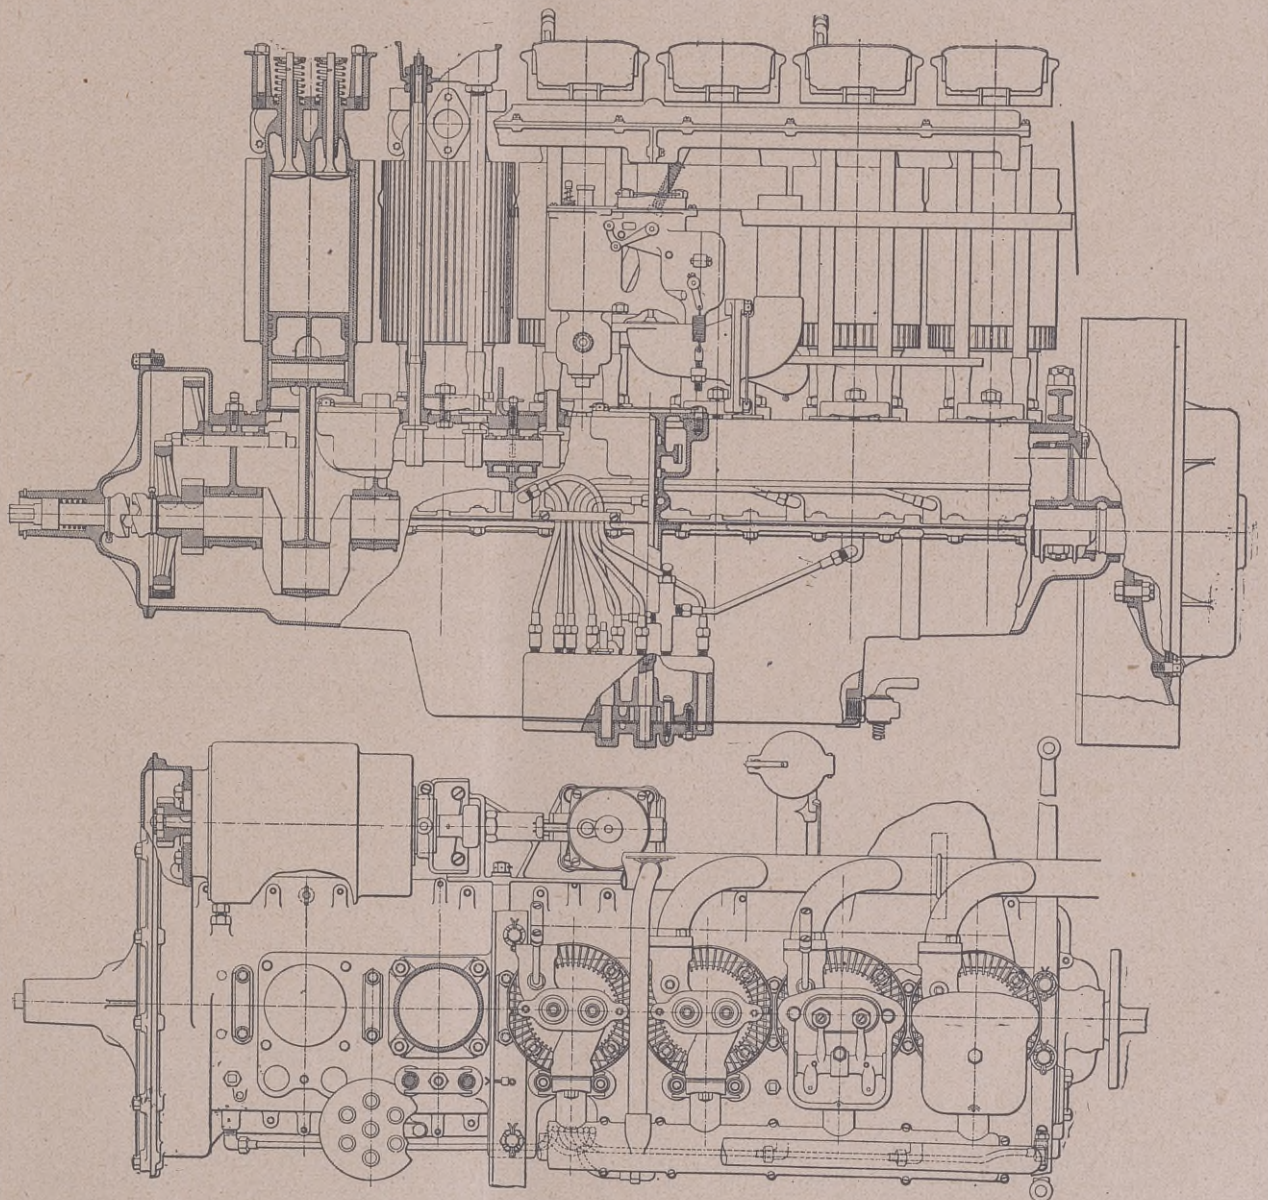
Seitenansicht und Grundriß des luftgekühlten Verbrennungsmotors.
